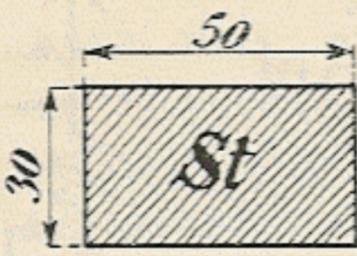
Die Stanniol- oder Aluminiumbelege.
